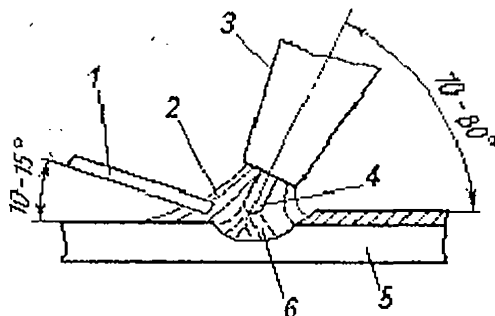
Схема дуговой сварки неплавящимся электродом в инертных газах:
